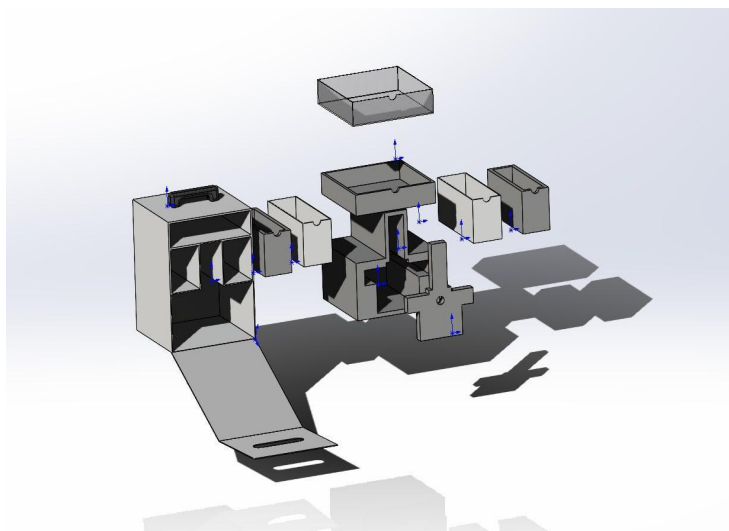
Поэлементная схема упаковки манипулятора Hobots D
